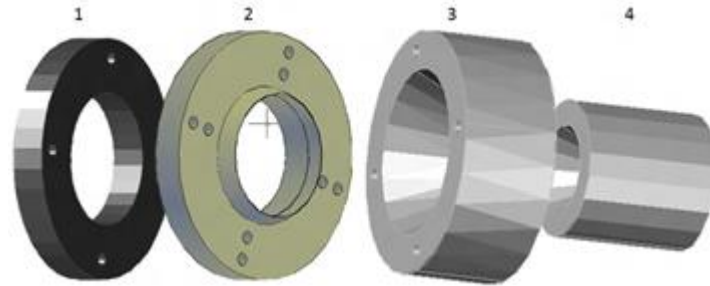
Vista 3D sólida del diseño del dado para espumas cilíndricas.
